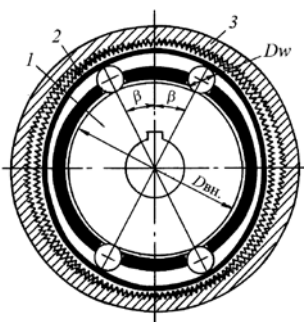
Поперечный разрез волновой передачи с планетарным генератором волн: 1 – планетарный генератор волн; 2 – гибкий элемент; 3 – жесткое колесо
